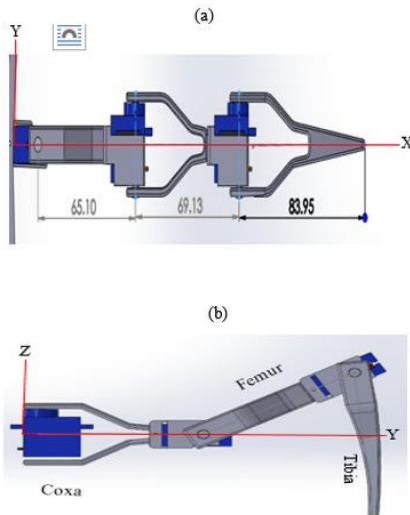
Vistas de la Pata (a) Plano YX, (b) Plano ZY. Fuente: Propia.
